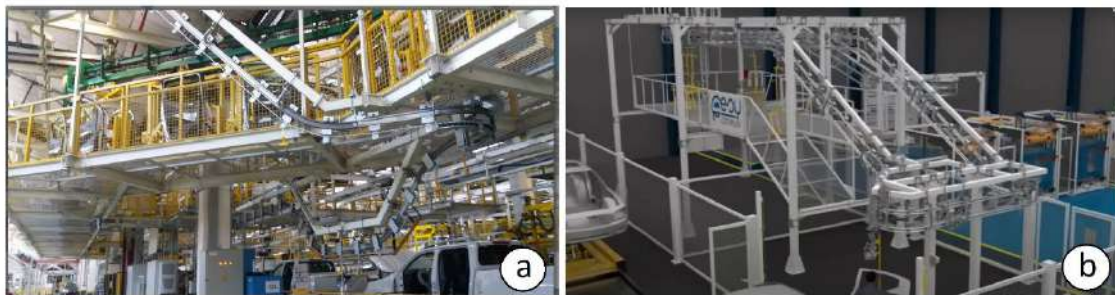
Ejemplo de estructuras soporte de transportadores aéreos (fuente: <https://esypro.com/soluciones/esyconveyor>). a) Lay-out de transportador aéreo en planta industrial de automóvil. b) Modelo 3D de estructura soporte para lay-out de transportador aéreo.
